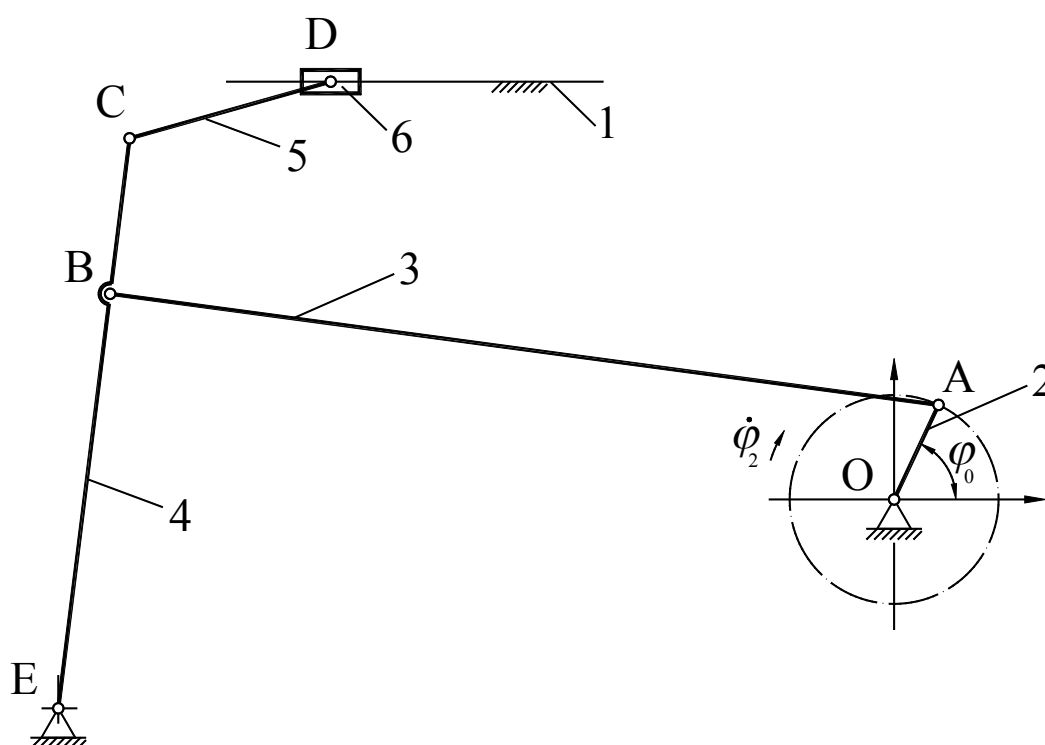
Кинематическая схема механизма подачи заготовок
